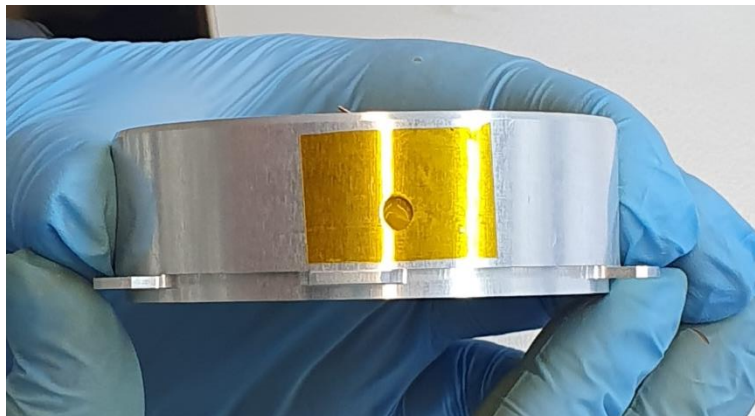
Корпус статора с закрытым отверстием для введения клея.
